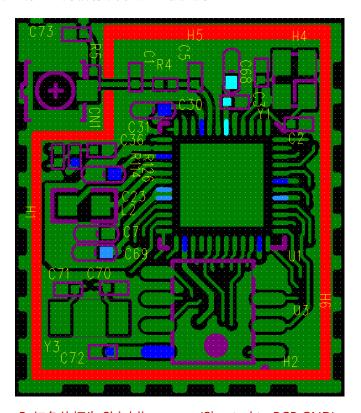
红色外框为 Shielding cover(Shorted to PCB GND)
